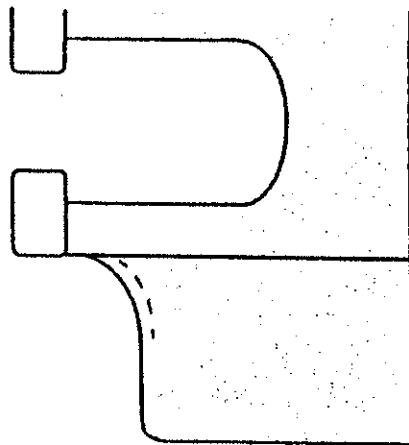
Контроль сварного соединения кронштейна гасителя колебаний с опорной плитой
